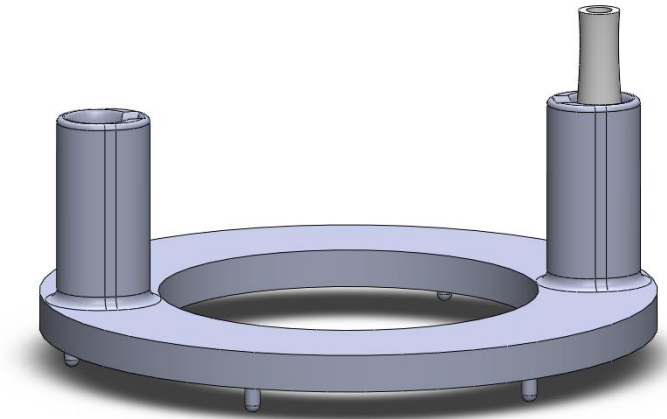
Přípravek pro robota se založenými součástmi pro jeden výrobek
